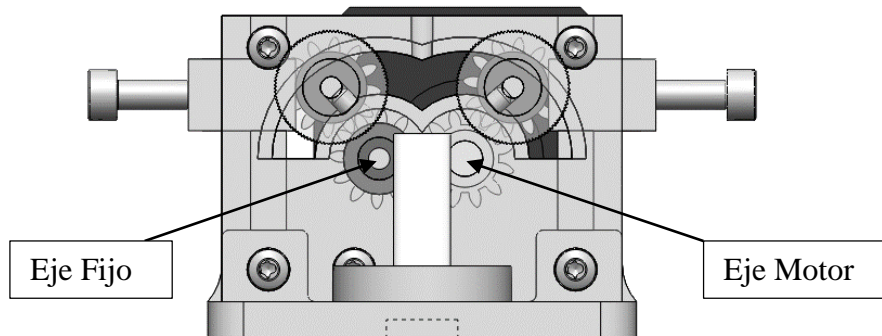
Eje de transmisión y eje fijo del extrusor de engranajes pivotantes (Versión 01)
